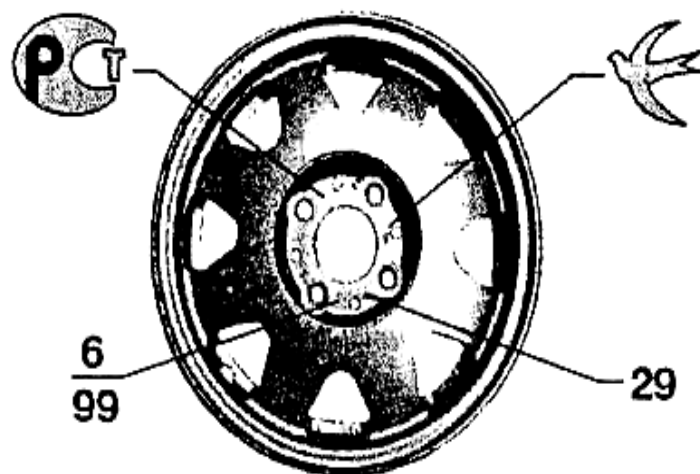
Маркировка диска колеса (по часовой стрелке):
